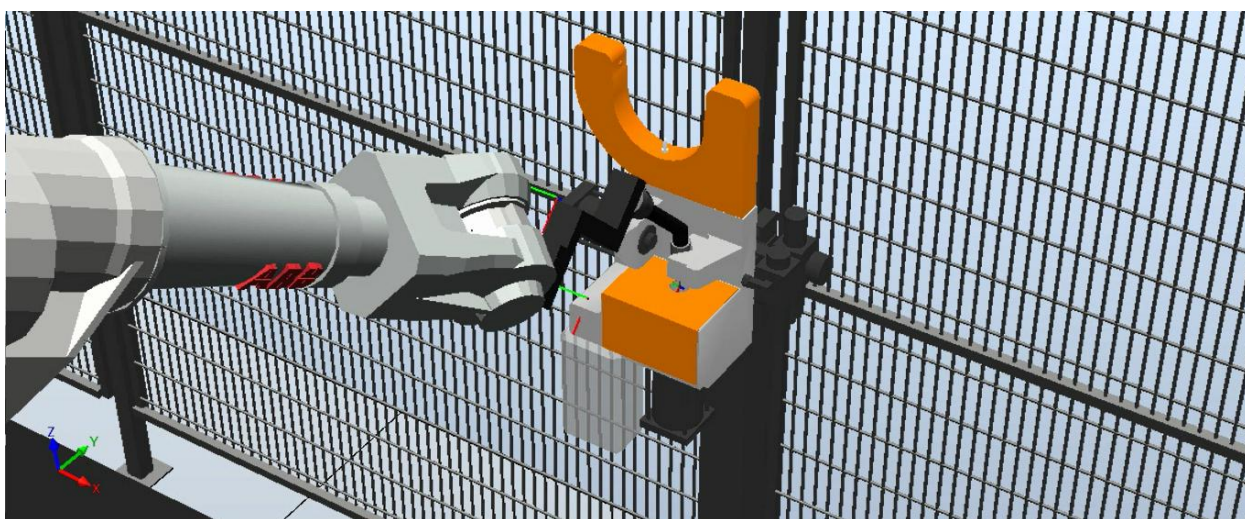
Limpieza en el Torch Cleaner del robot IV tras finalizar la soldadura.
